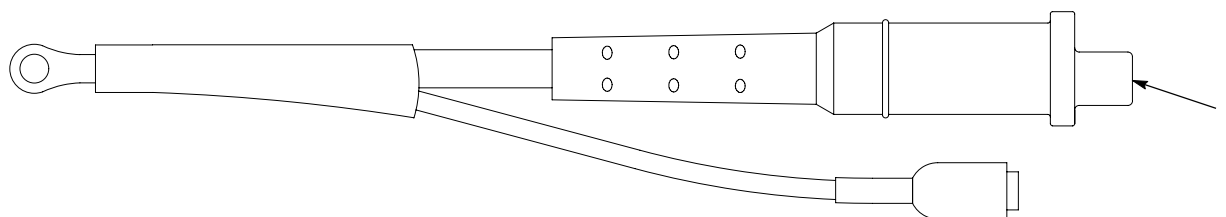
Ремонтные комплекты для рукоятки и спускового крючка
